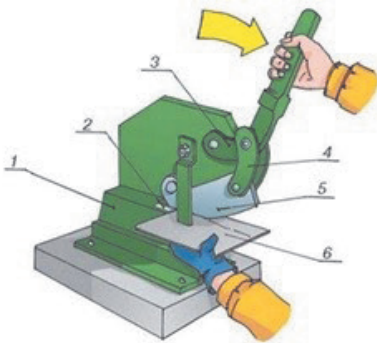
Настільні ручні важільні ножиці: 1 — основа ножиць; 2 — нижній нерухомий ніж; 3 — важіль; 4 — з'єднувальна планка; 5 — верхній рухомий ніж; 6 — заготовка
